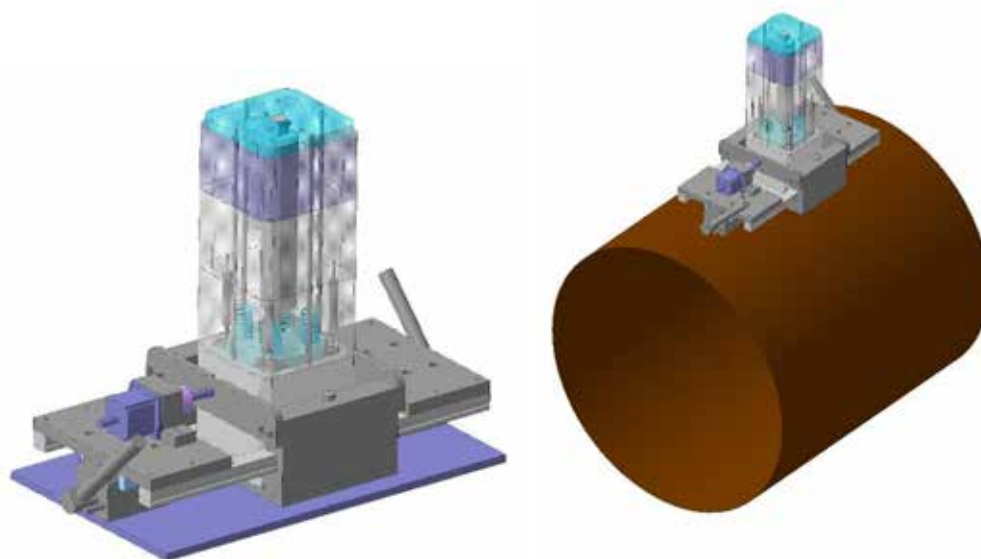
Расположение iPoRTH на плоской и цилиндрической поверхностях
